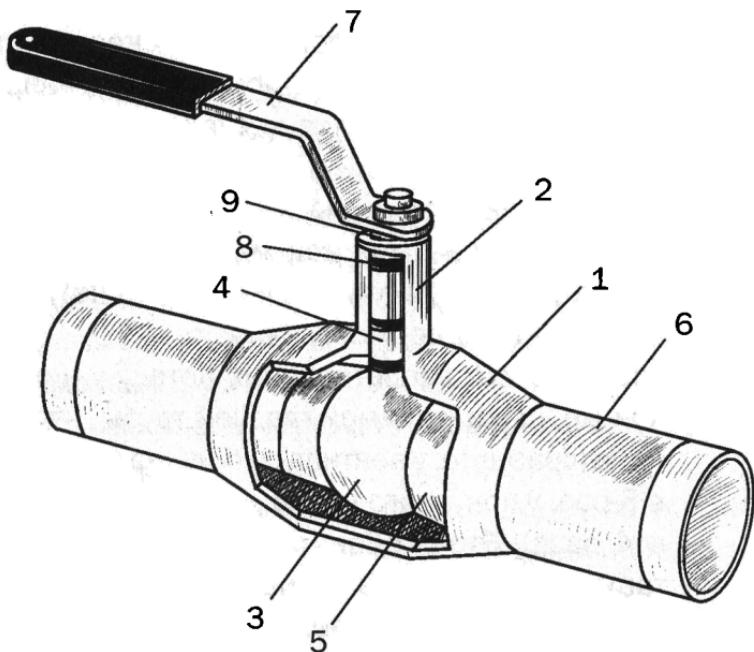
Конструкция шарового крана: 1 — корпус; 2 — корпус штока; 3 — шар; 4 — шток; 5 — уплотнение; 6 — патрубок; 7 — рукоятка; 8 — о-образное кольцо; 9 — уплотнительная втулка
